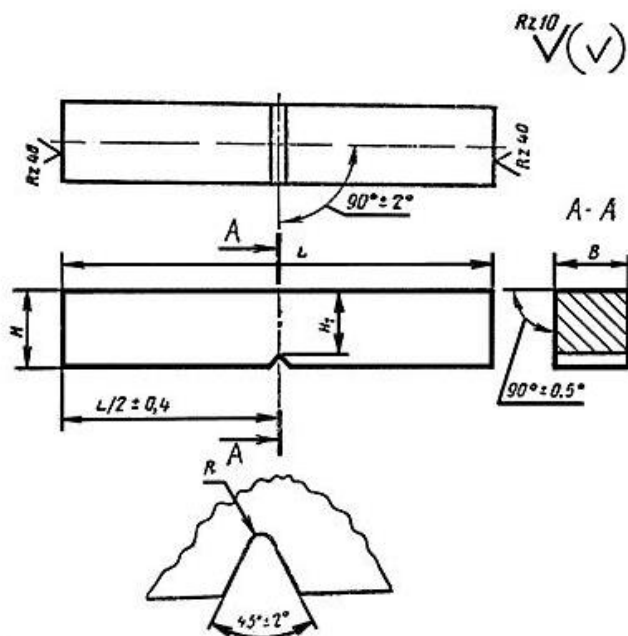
Образец для испытания на ударный изгиб с концентратором вида V
